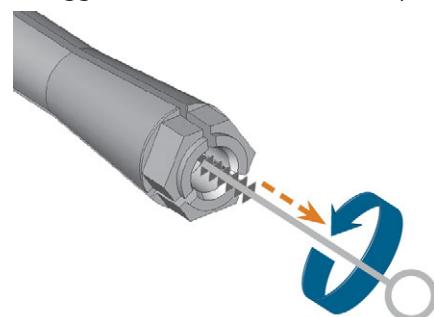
PULIZIA DELLA PINZA DI SERRAGGIO
